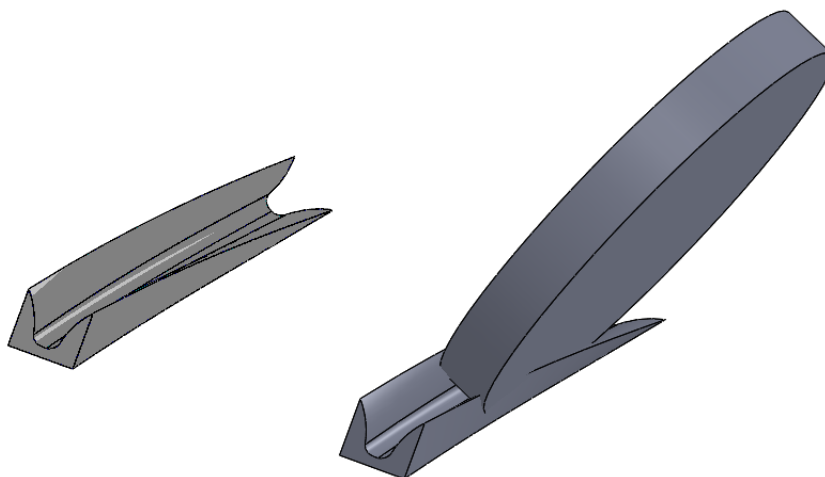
Фрагмент зубчатого колеса в области впадины его зуба и размещение на нем фрагмента с заготовкой фрезы
